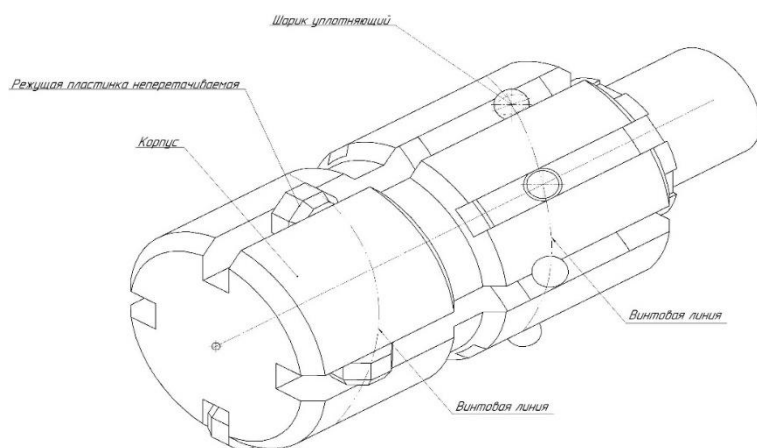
Комбинированная развертка с рабочими элементами, расположенными по винтовой линии
